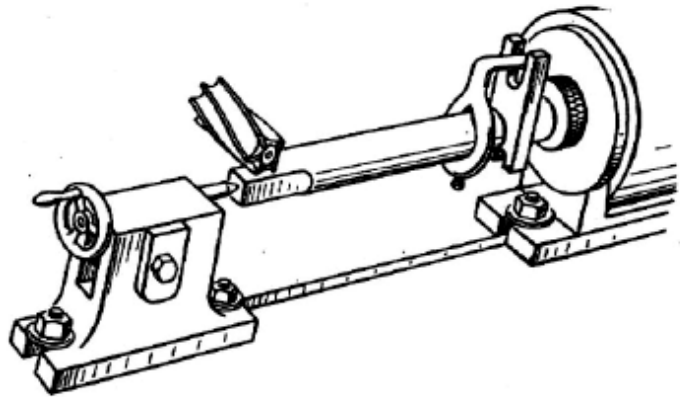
Фрезерування квадрата кінцевою фрезою
